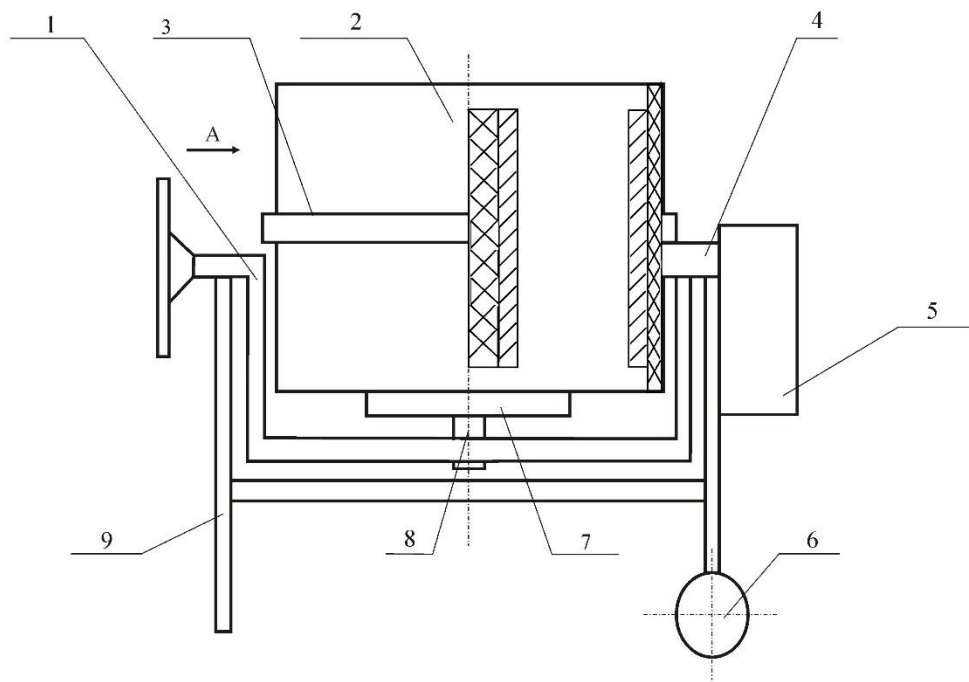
Фронтальный разрез установки магнитной обработки клубней картофеля
